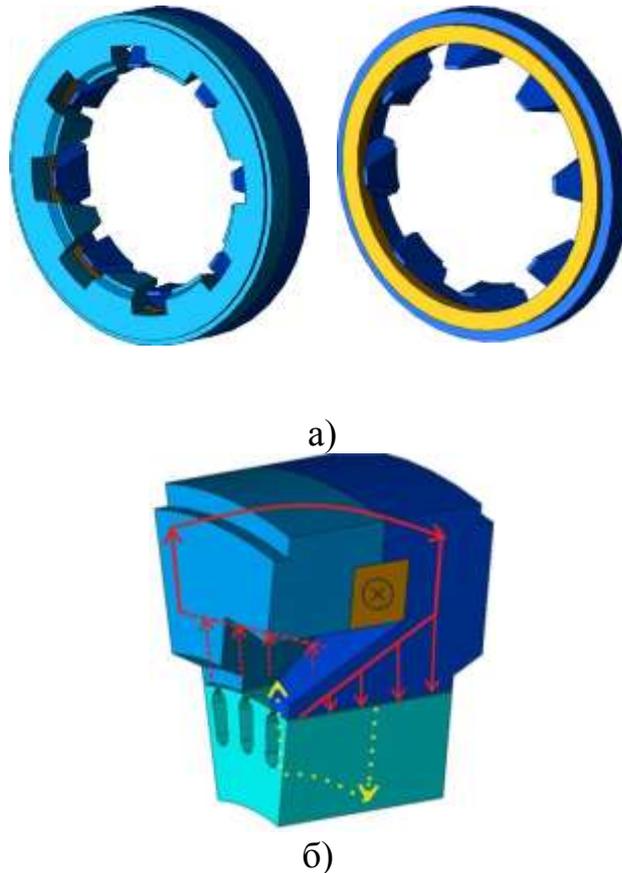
Конструкция возбuditеля с зубчатым статором: (а) детали индуктора и (б) траектории линий потока в конструкции
